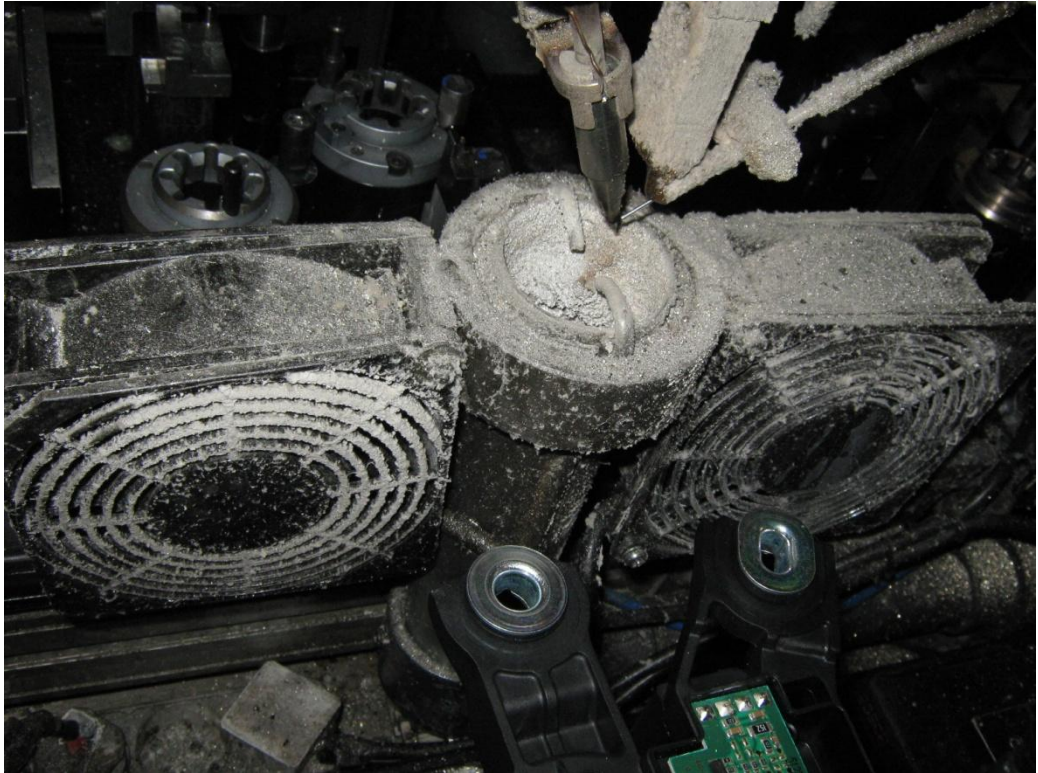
Foto cabezales de soldadura puesto 2.9
